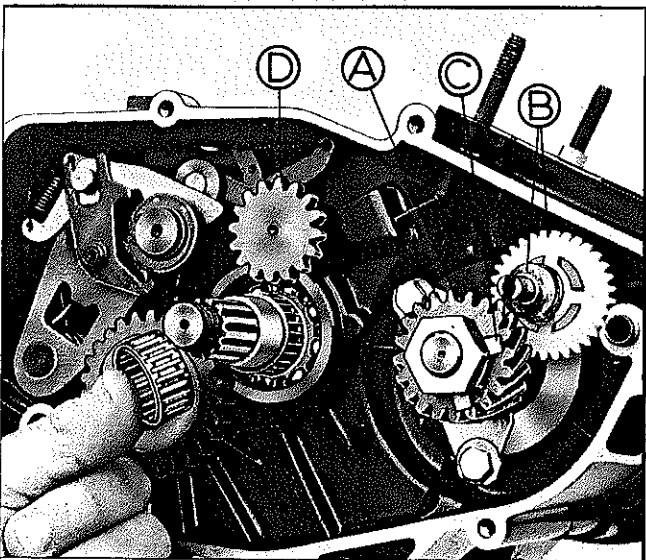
A. ENGRENAGEM DO VIRABREQUIM
